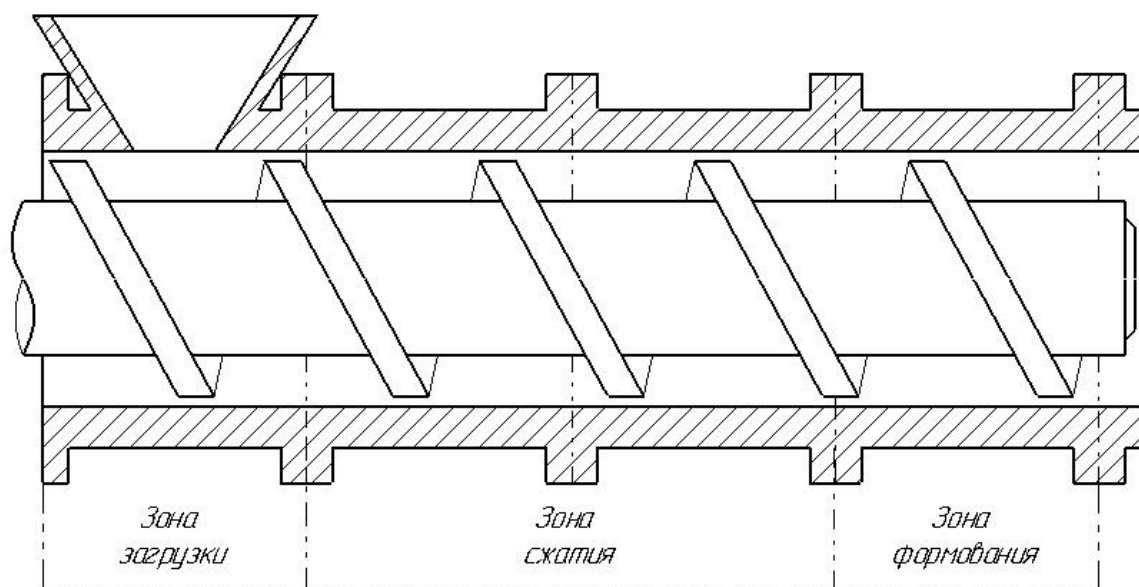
Конструкция шнекового пресса фрезформовочной машины
